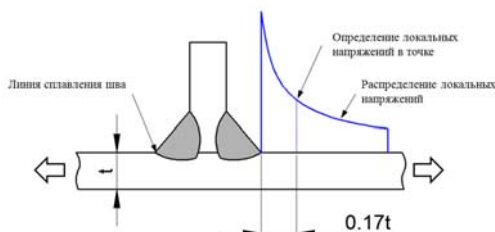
Схема определения локальных напряжений в зоне сварного соединения
